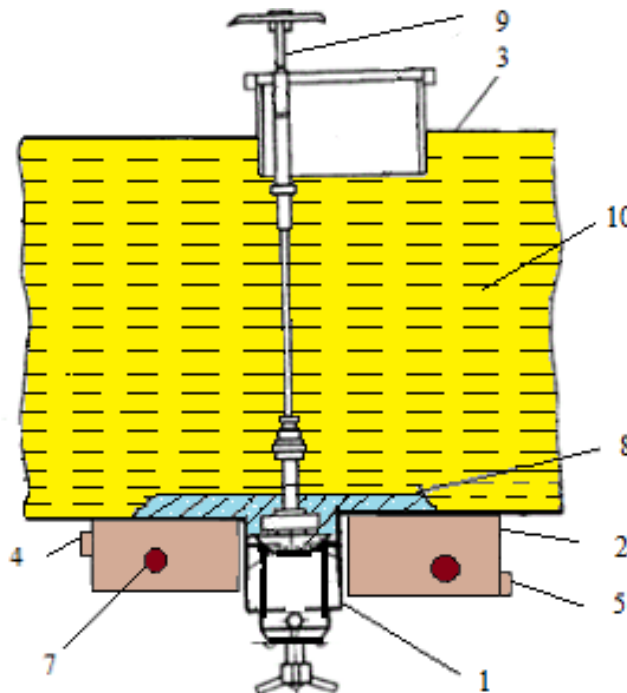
Разрез средней части котла цистерны с верхним наливным люком, нижним сливным прибором и обогревательным кожухом
